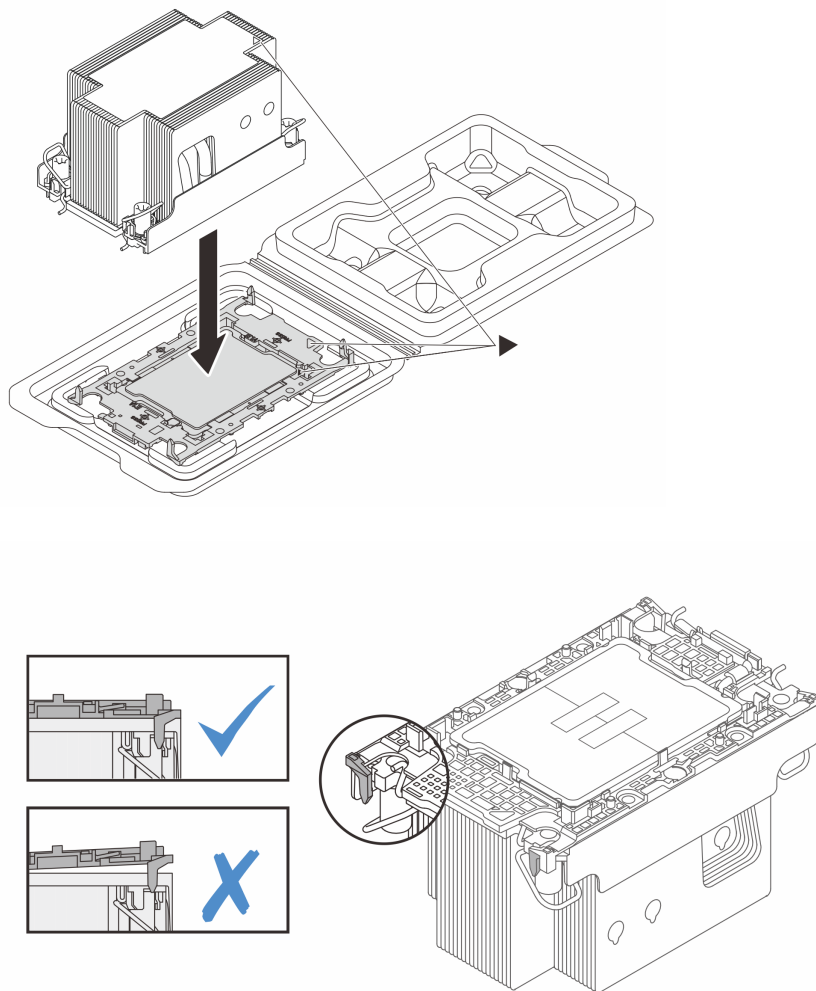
Assemblage du module de processeur-dissipateur thermique avec le processeur dans le plateau d'expédition
